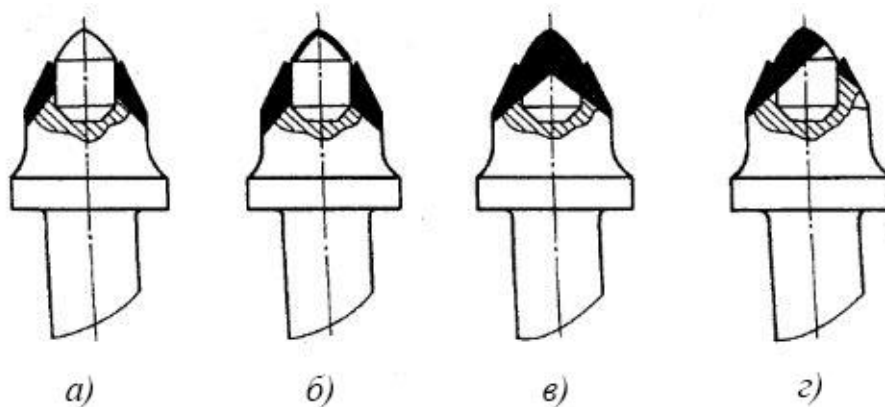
Формы износа поворотных резцов: а) износ головки державки; б) неравномерный износ головки державки и твердосплавной вставки; в) равномерный износ головки державки и твердосплавной вставки; з) односторонний износ.
